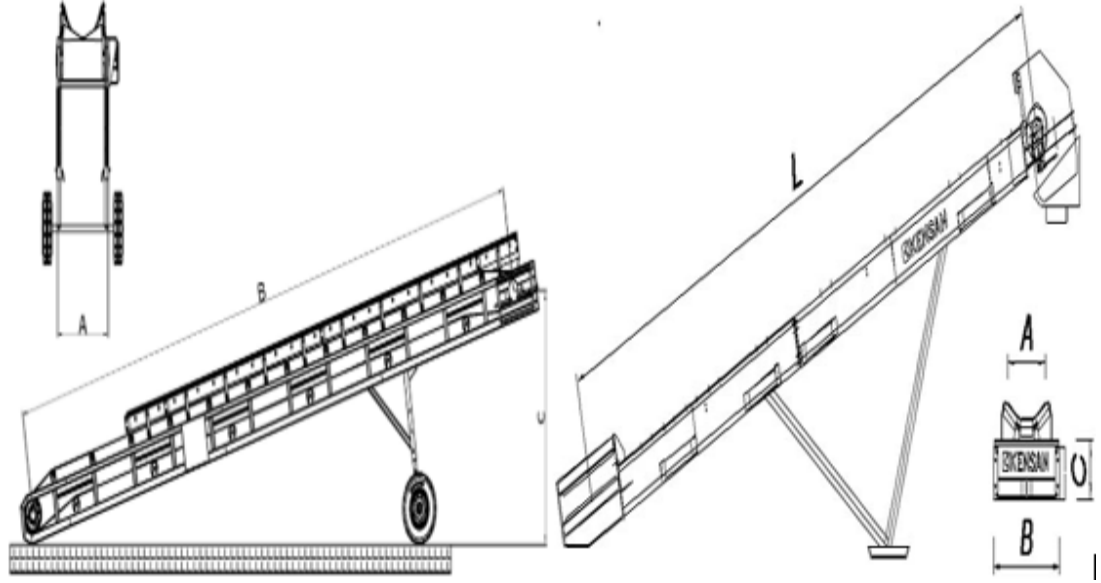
Taşıyıcı konveyör makinesi görselleri
